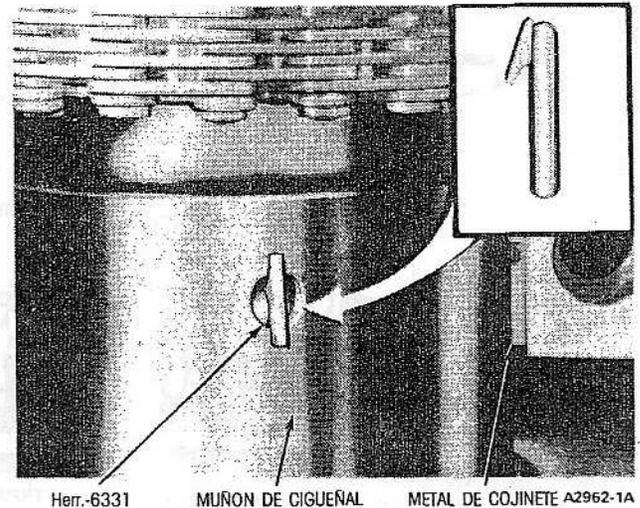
Remoción o Instalación del Metal Superior del Cojinete Principal
